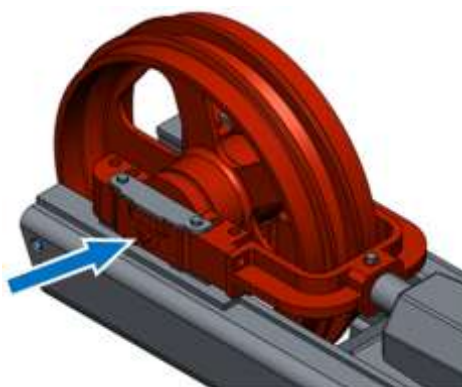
Внешний осмотр и процедура смазки натяжного колеса
